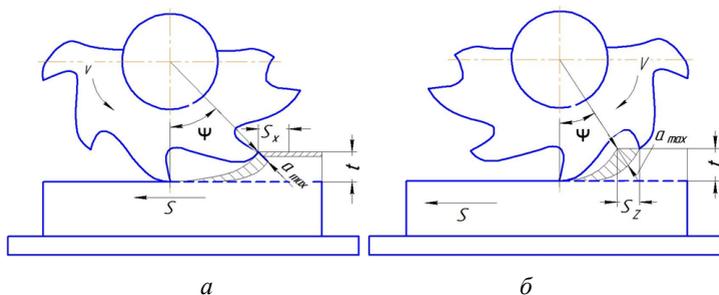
Схемы встречного (а) и попутного фрезерования (б)
